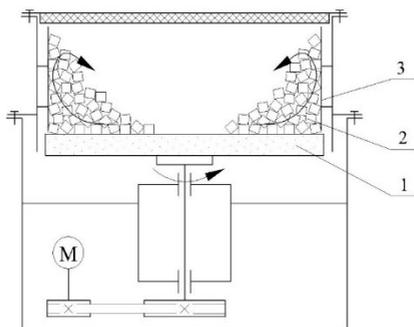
Схема станка для предварительного шлифования шариков из кубиков
